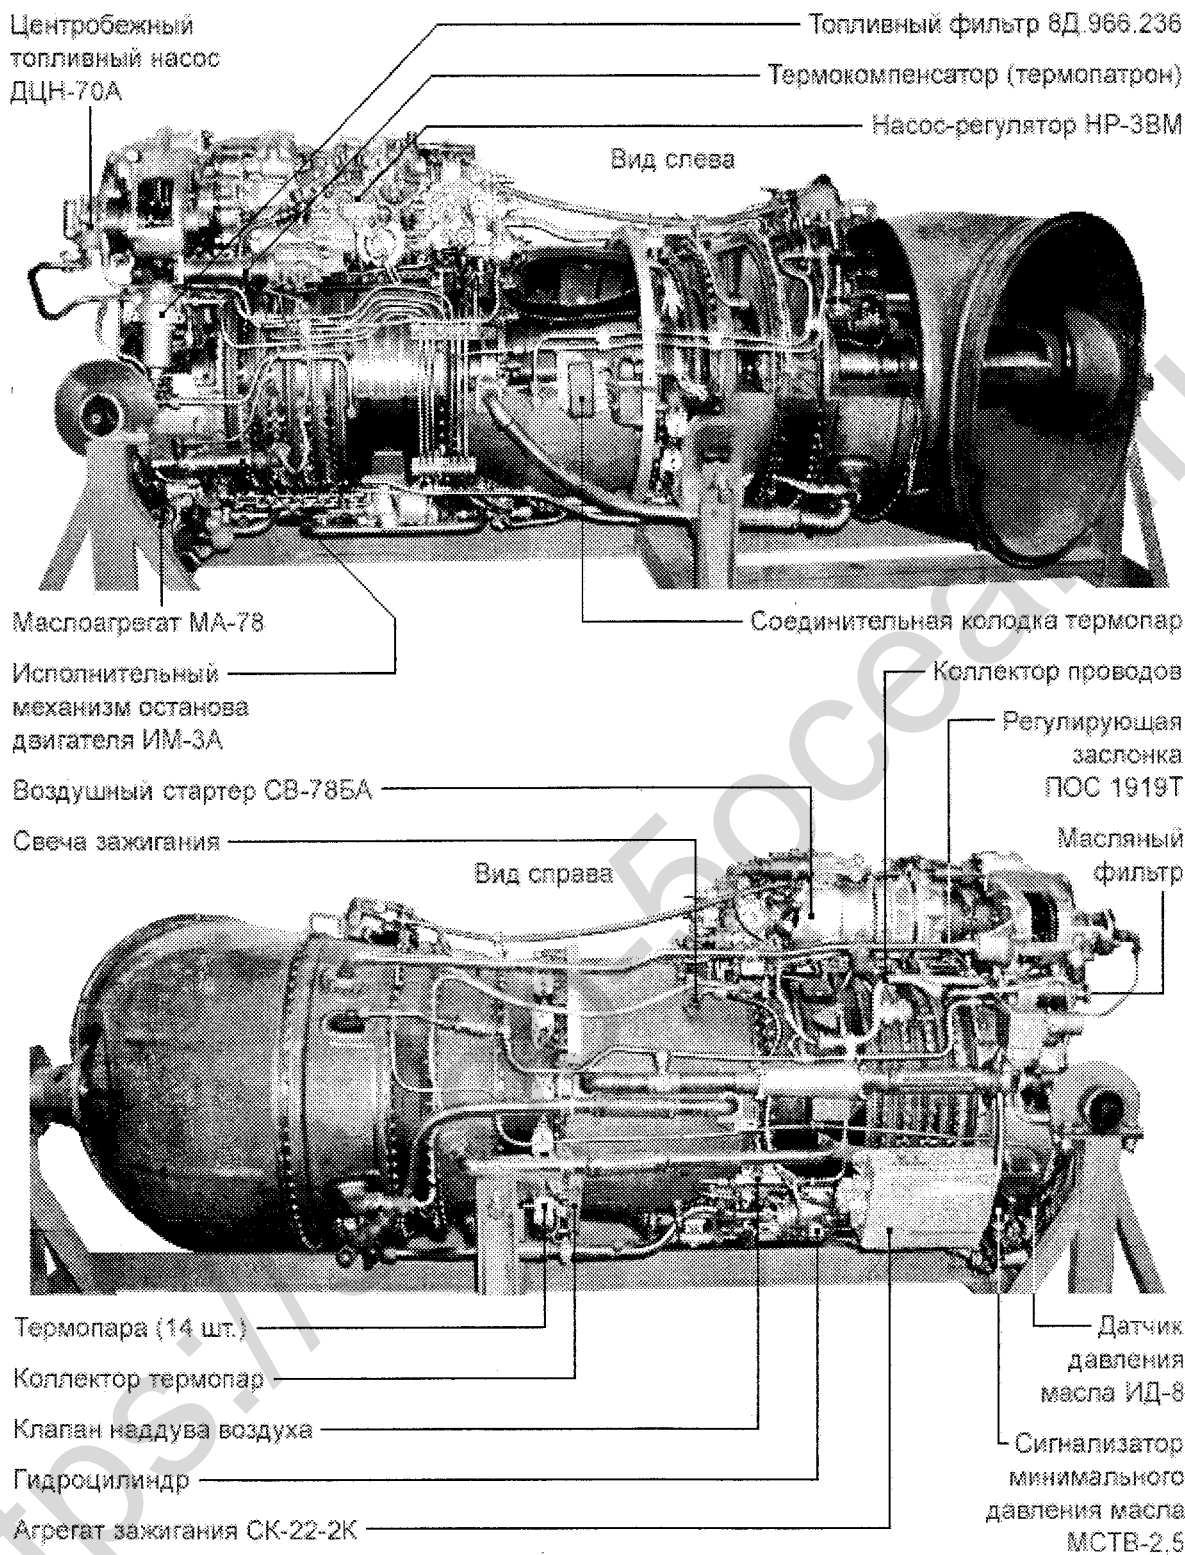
Общий вид двигателя ТВ3-117В
